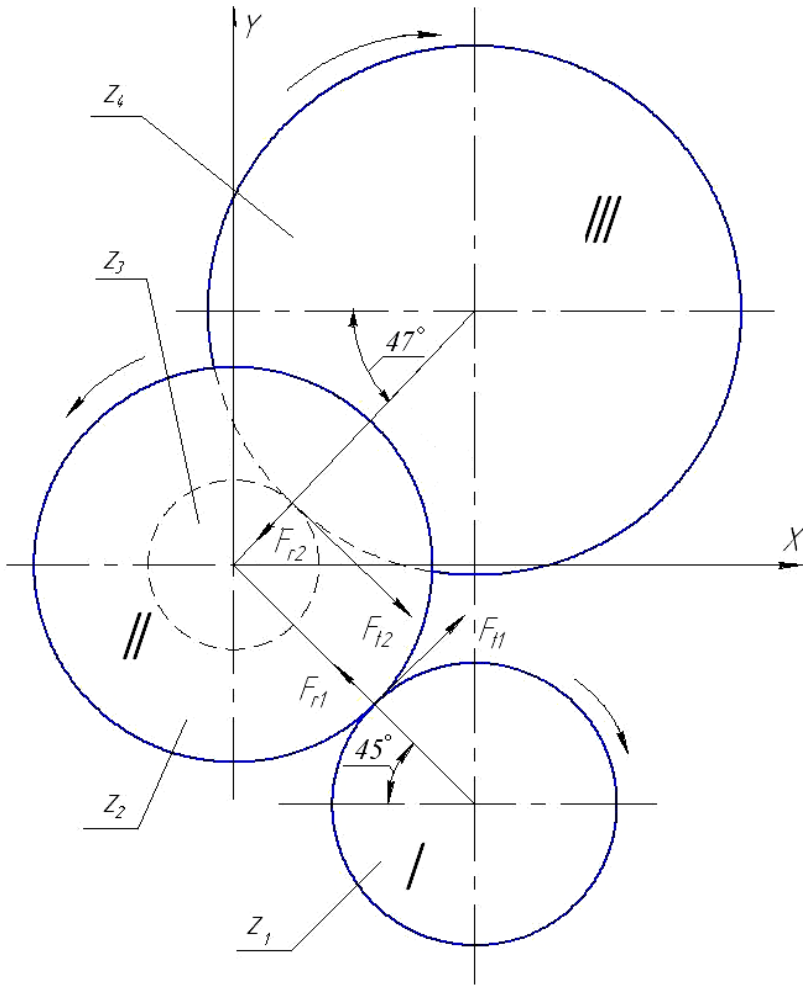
Расчетная схема для определения сил в зацеплениях зубчатых колес, действующих на наиболее нагруженный вал шпиндельной бабки сверльно-фрезерно-расточного станка с ЧПУ
